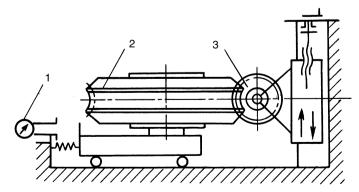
Схема измерения червячных колёс на межцентромере с помощью приспособления
